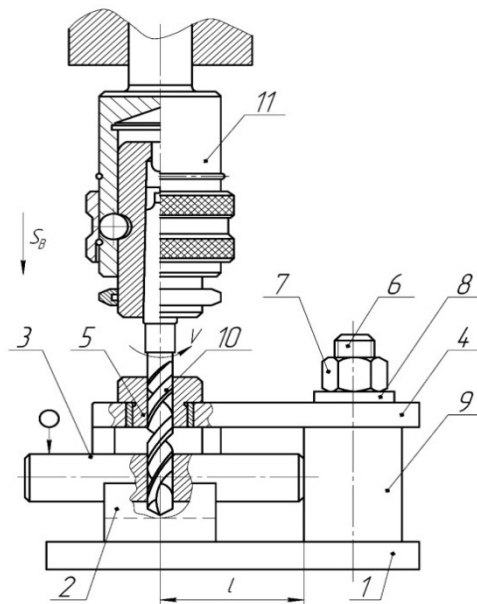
Схема операции: 1 – плита прямоугольная; 2 – призма; 3 – заготовка; 4 – планка; 5 – быстросменная кондукторская втулка; 6 – болт; 7 – гайка; 8 – шайба; 9 – стойка; 10 – сверло; 11 – патрон.
